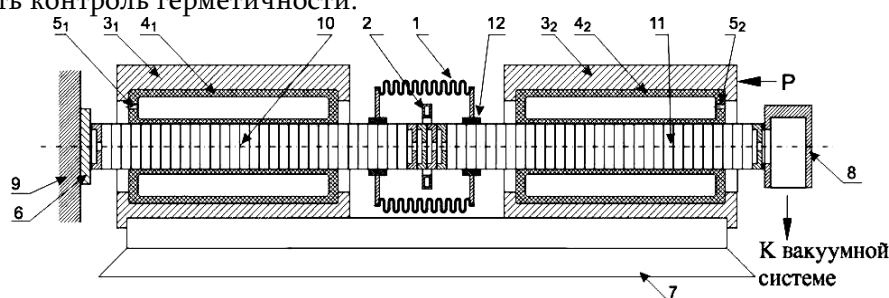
Схема установки для диффузионной сварки длинномерных изделий:
